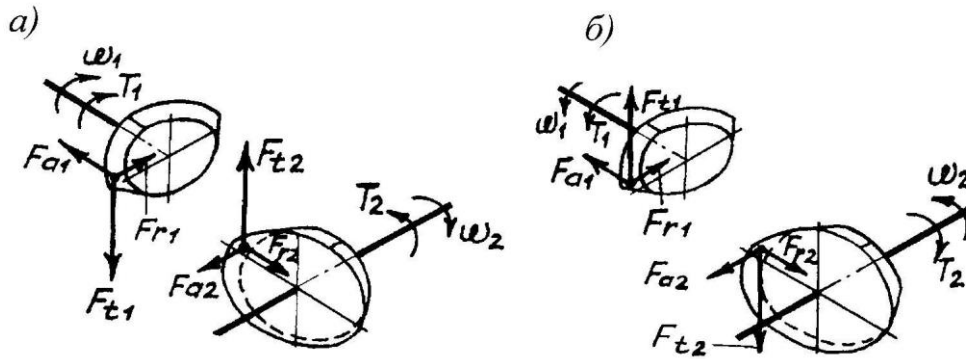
Схема сил в зацеплении прямозубой конической зубчатой передачи
